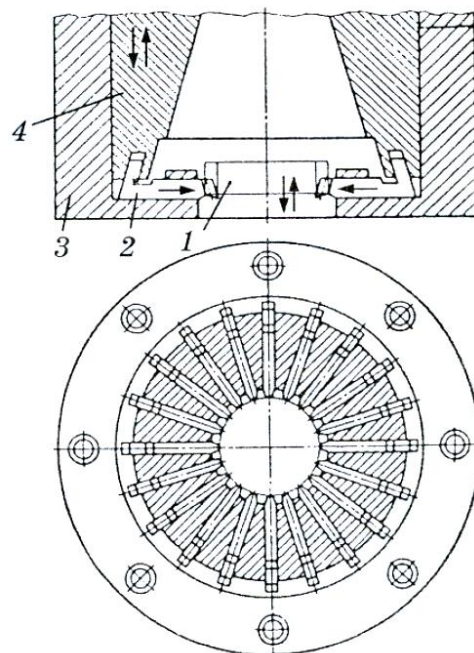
Многорезцовая зубодолбежная головка: 1 – обрабатываемое зубчатое колесо; 2 – резцы; 3 – корпус головки; 4 – конусное кольцо
